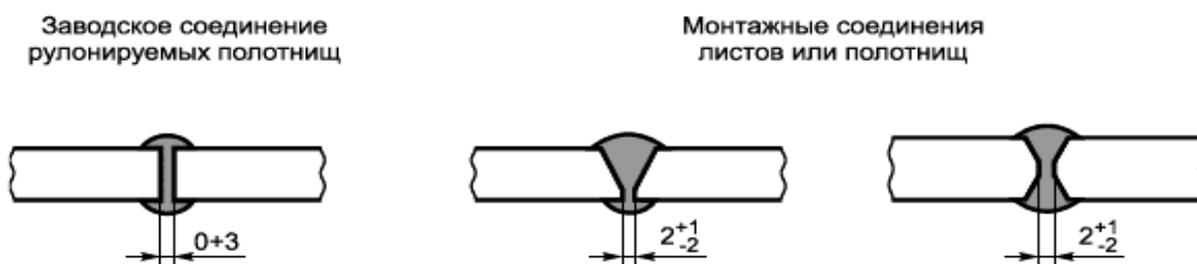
Рекомендуемые виды вертикальных сварных соединений стенки
